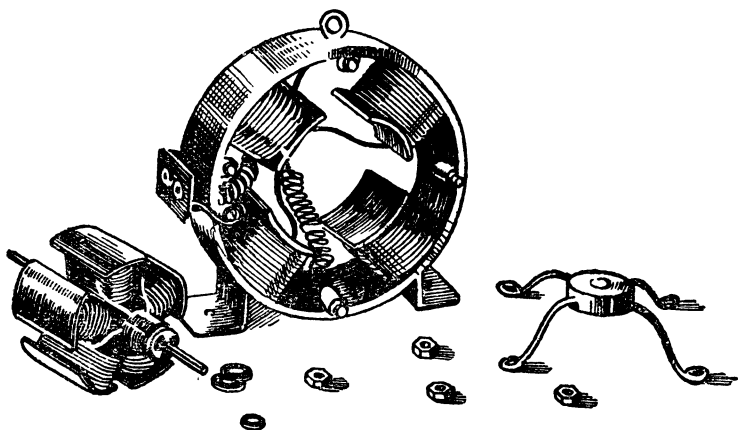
Детали двигателя с пятиполюсным якорем. Слева — якорь; в середине — статор; справа — передняя крышка.
